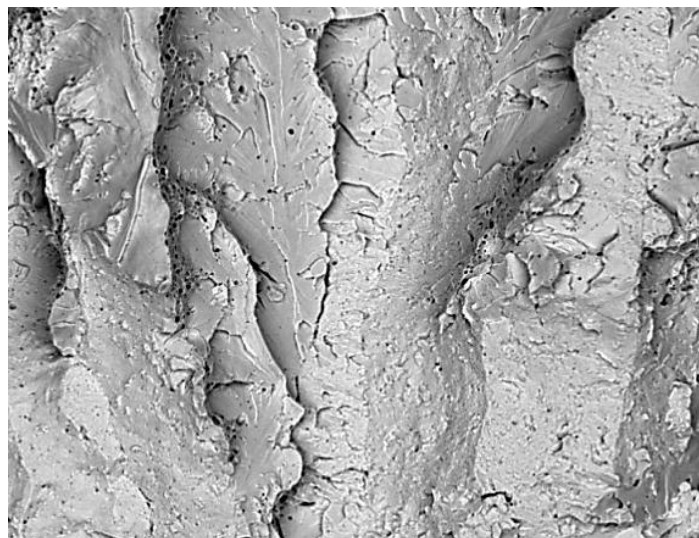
Появление в изломе металла шва междендритного хрупкого разрушения наряду со сколом: РЭМ, x500 [The appearance of the dendritic brittle fracture along with the chip in the fracture of the weld metal: x500]
